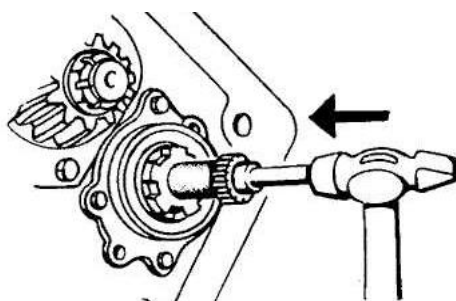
Запрессовка внутреннего вала в корпус КПП
